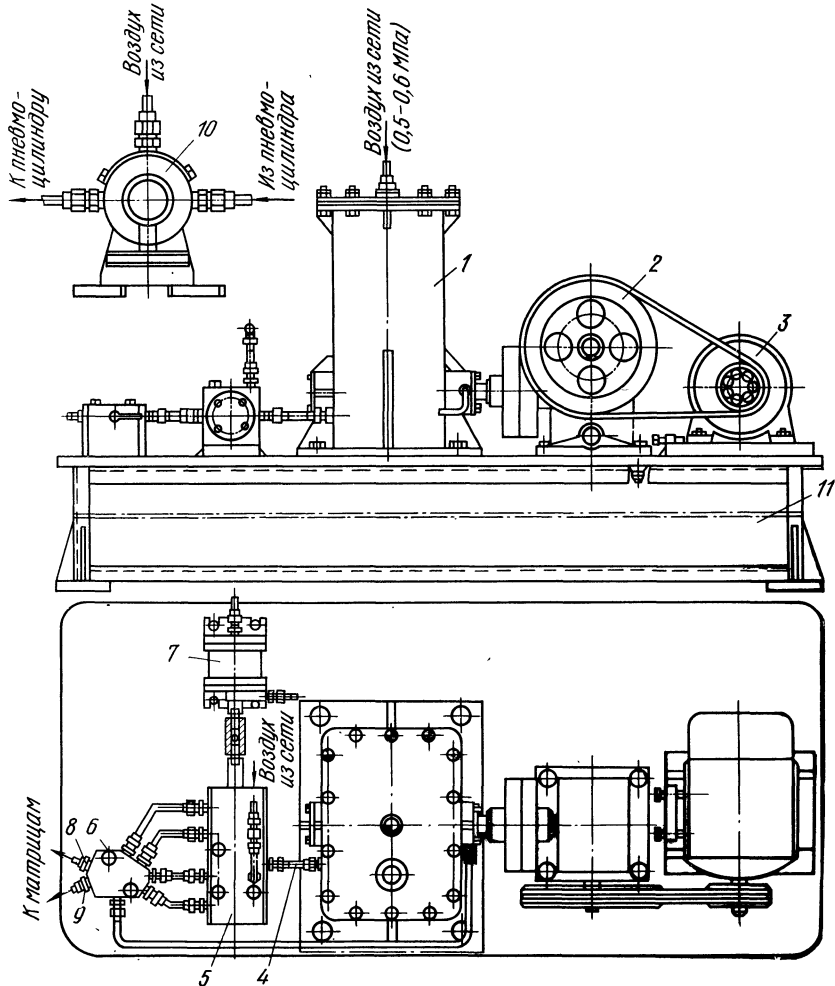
Стационарная установка для подачи смазки при штамповке [433]
